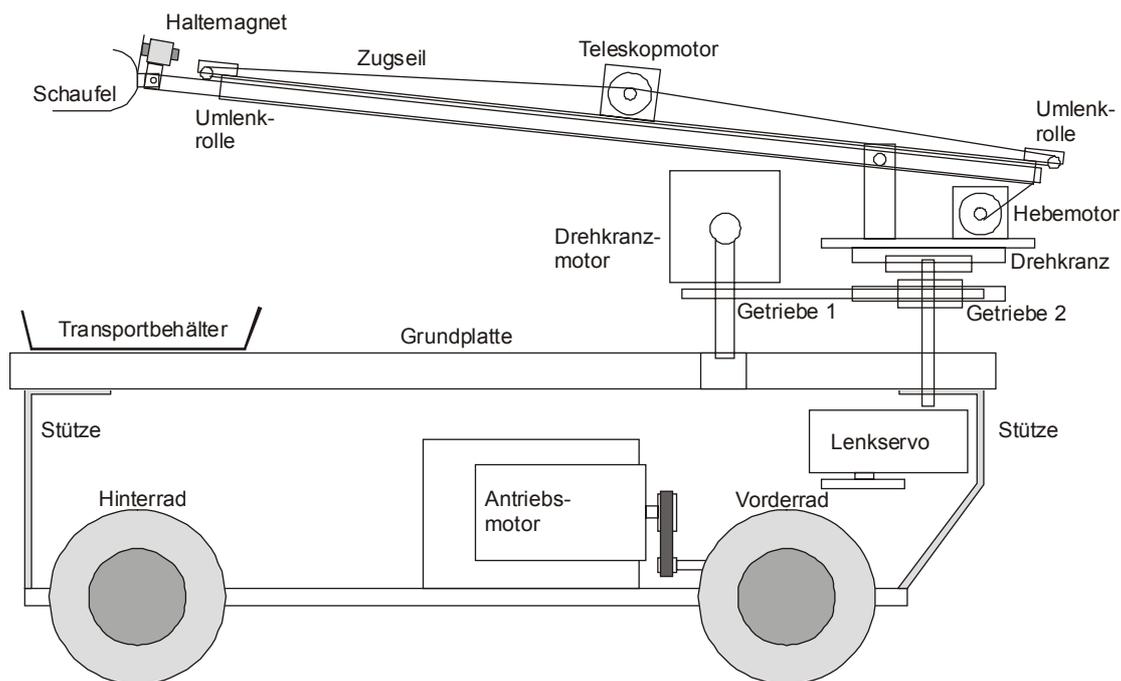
Seitenansicht unseres Fahrzeugs mit allen Aufbauten
